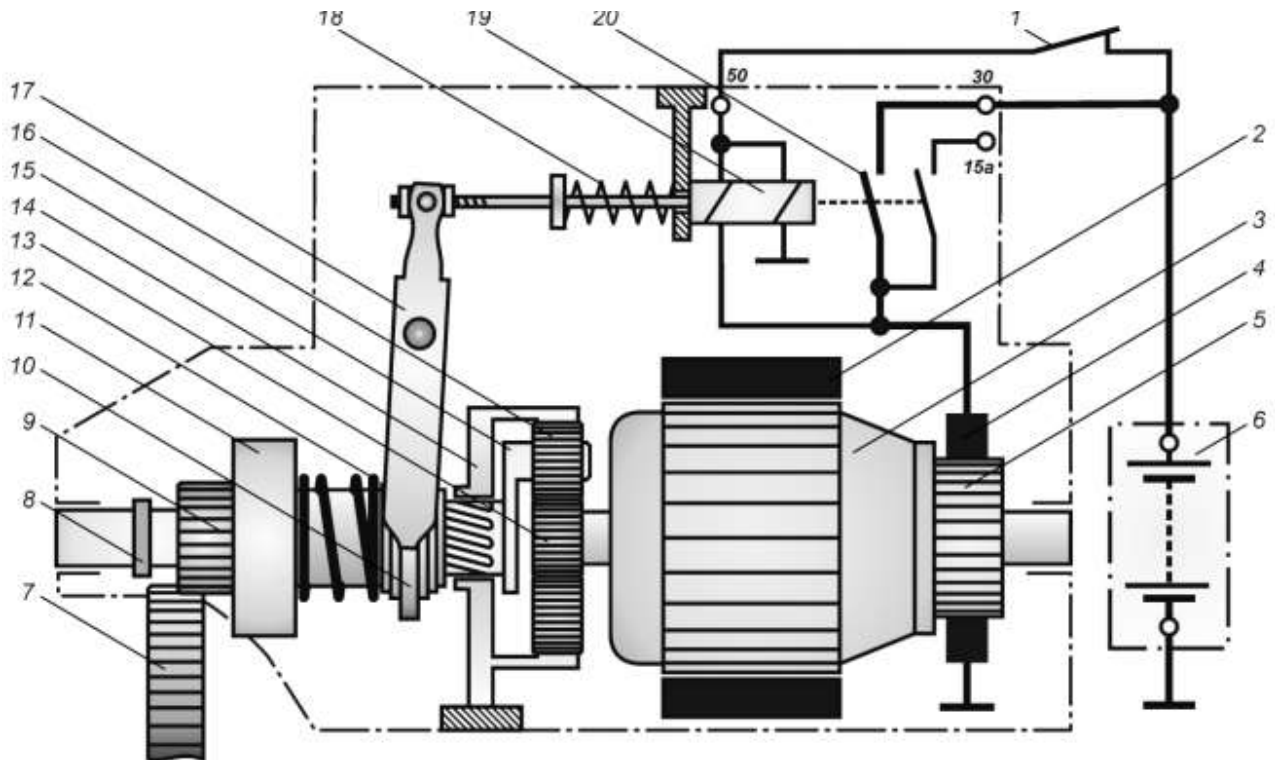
Схема стартера з постійними магнітами і планетарним редуктором:
